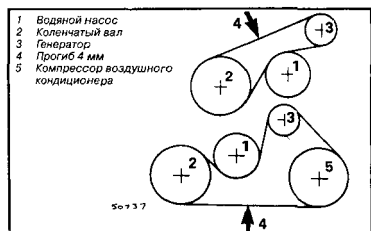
Регулировка натяжения многоручьевого клиновидного ремня (двигатель OHC)
